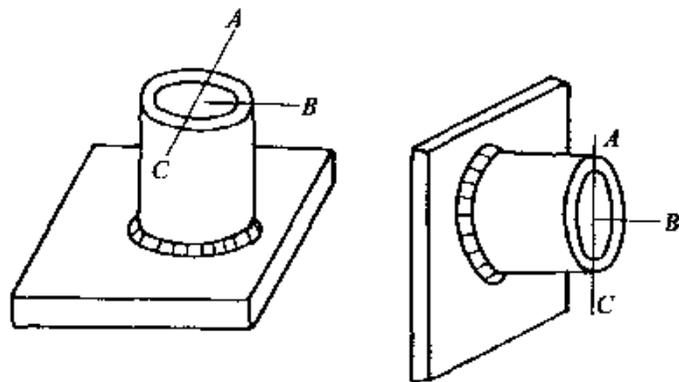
管板全焊透角焊缝试件断面检验位置
